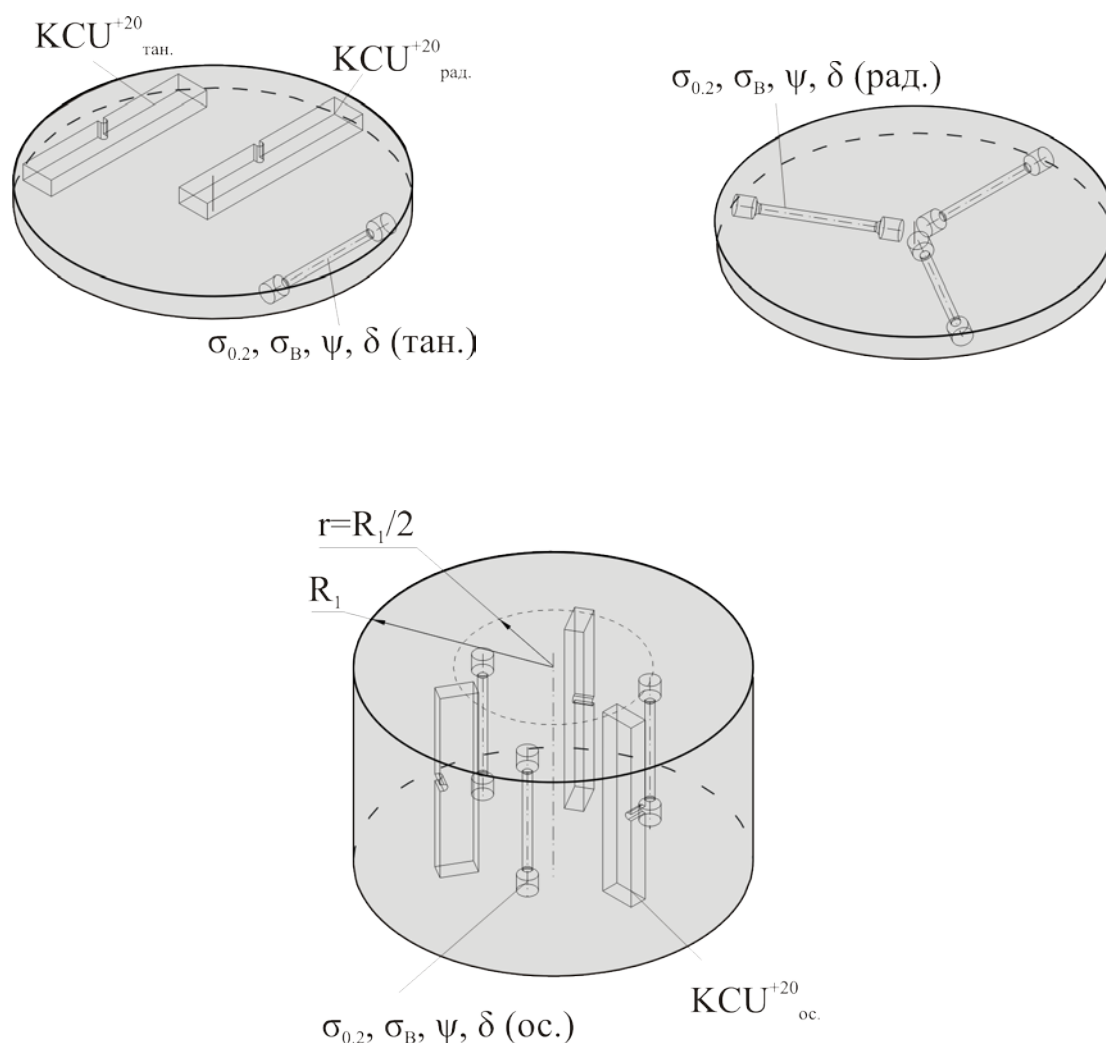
Схема вырезки образцов для механических испытаний из литой заготовки
